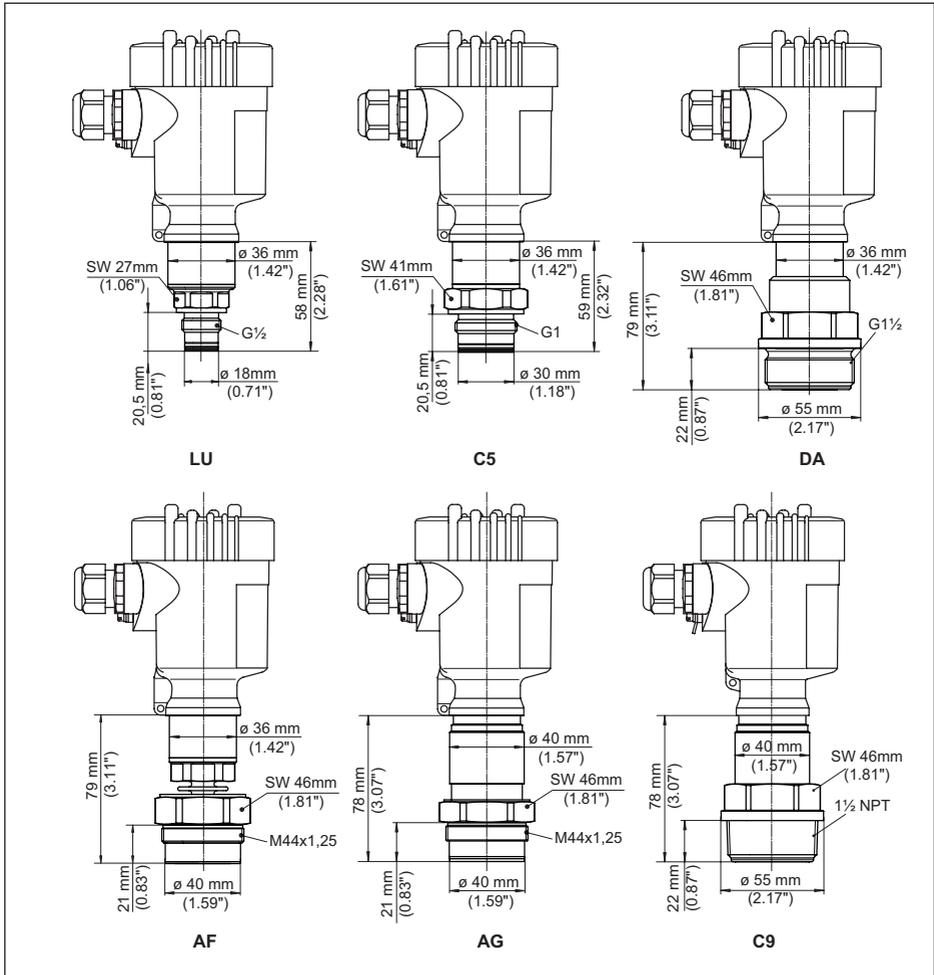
VEGABAR 83, Gewindeanschluss frontbündig
